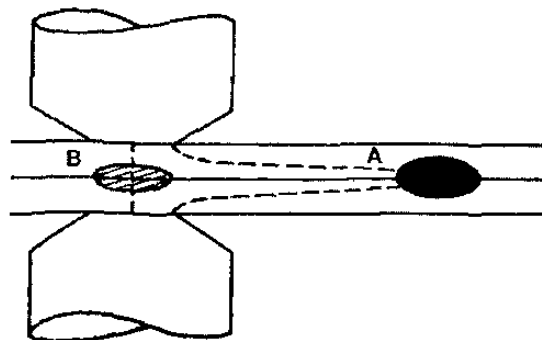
Efecto del desvío de corriente hacia el botón de soldadura previamente formado⁽¹⁾.
